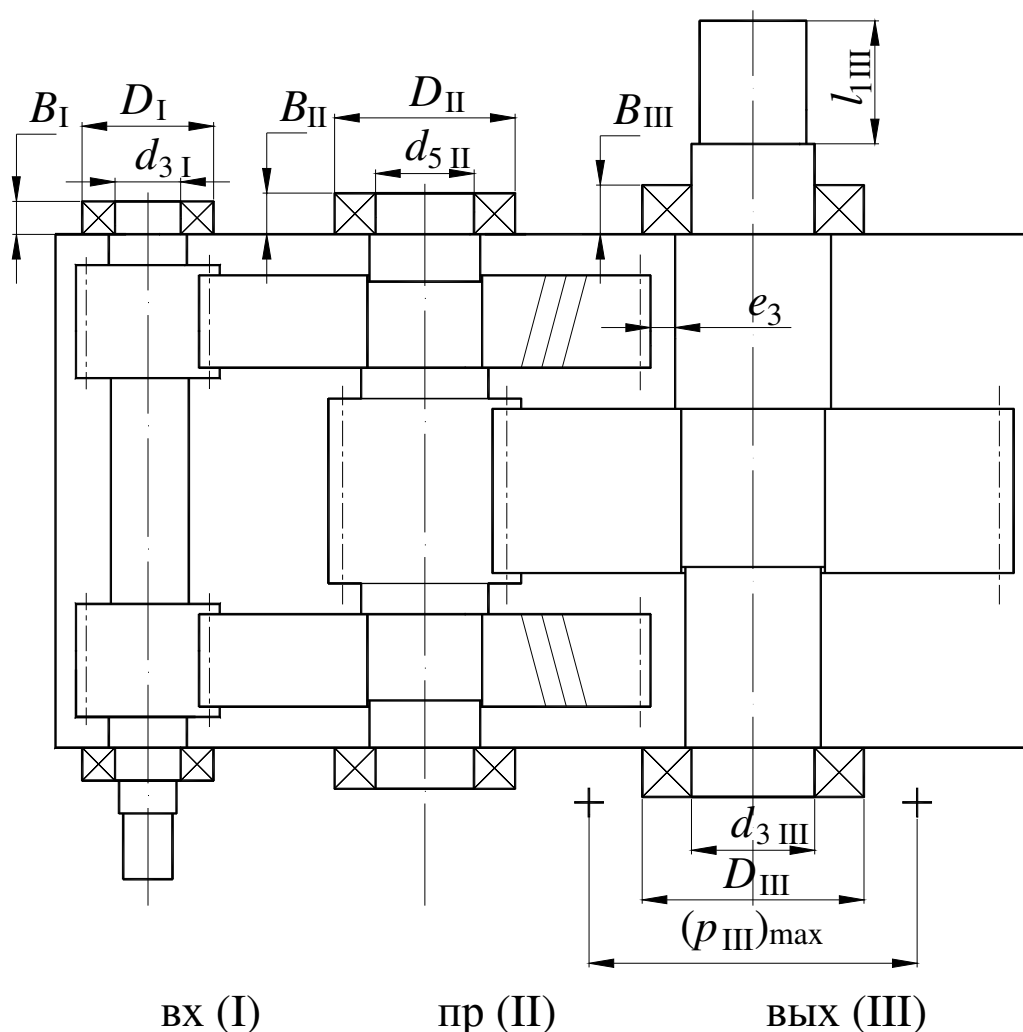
Окончательный результат составления эскизной компоновки цилиндрического редуктора по схеме раздвоенный шеврон
